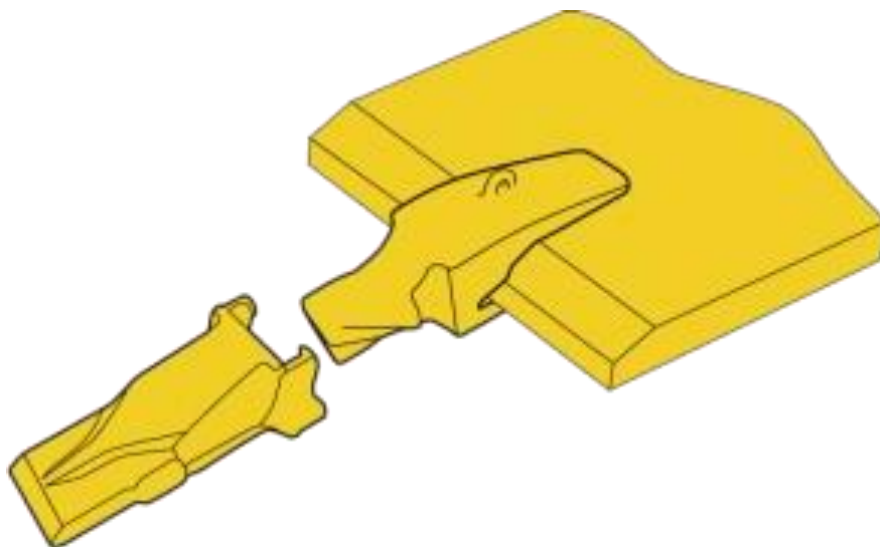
Загальний вигляд зуба ковша екскаватора.[5]
